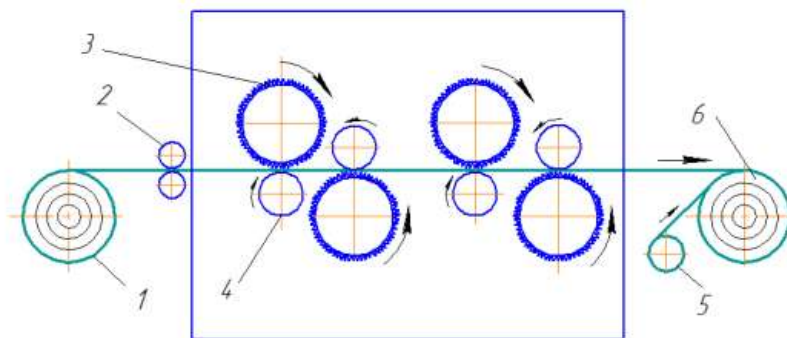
Схема установки для двусторонней зачистки составляющих слоистых металлов в рулоне: 1 - размотыватель с рулоном ленты; 2 – задающее устройство; 3 – барабан со щетками; 4 – прижимной барабан; 5 – размотыватель с защитной бумагой или пленкой; 6 – наматывающий барабан.
